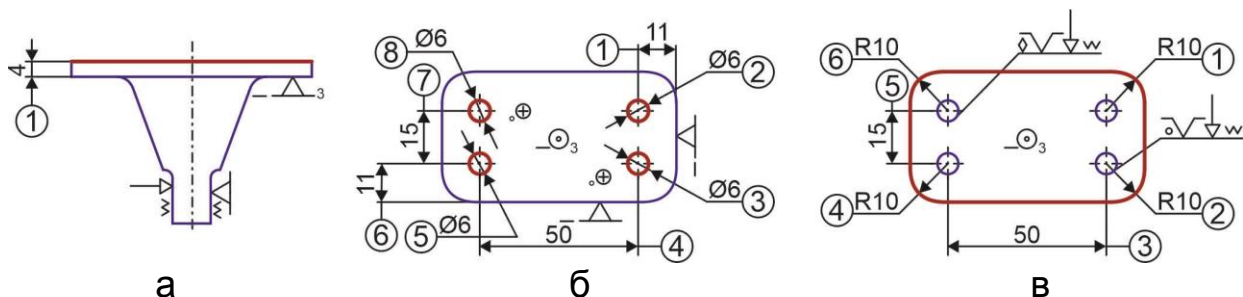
Приклади операційних ескізів для механічної обробки: а – фрезерування площини; б – свердління чотирьох отворів; в – фрезерування контуру
